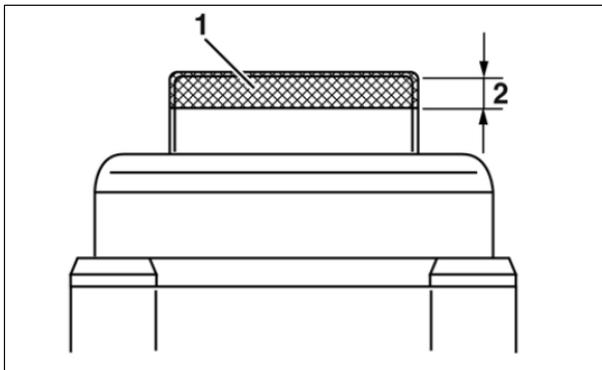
Zona de pintado para el borde cilíndrico de la membrana del sensor
